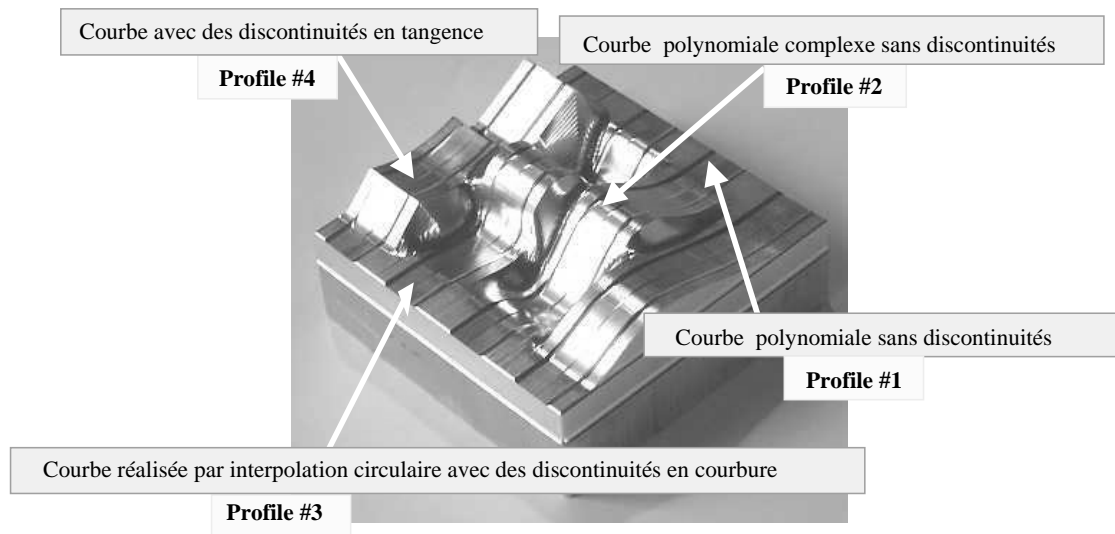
Pièce test pour l'usinage de formes complexes [Terrier04]
